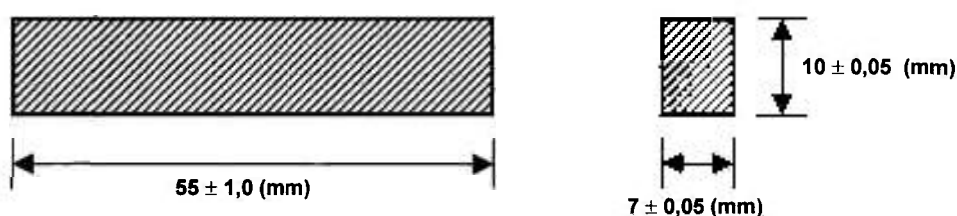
Dimensões do corpo de prova para ensaio de impacto Charpy sem entalhe [118,125,126].
